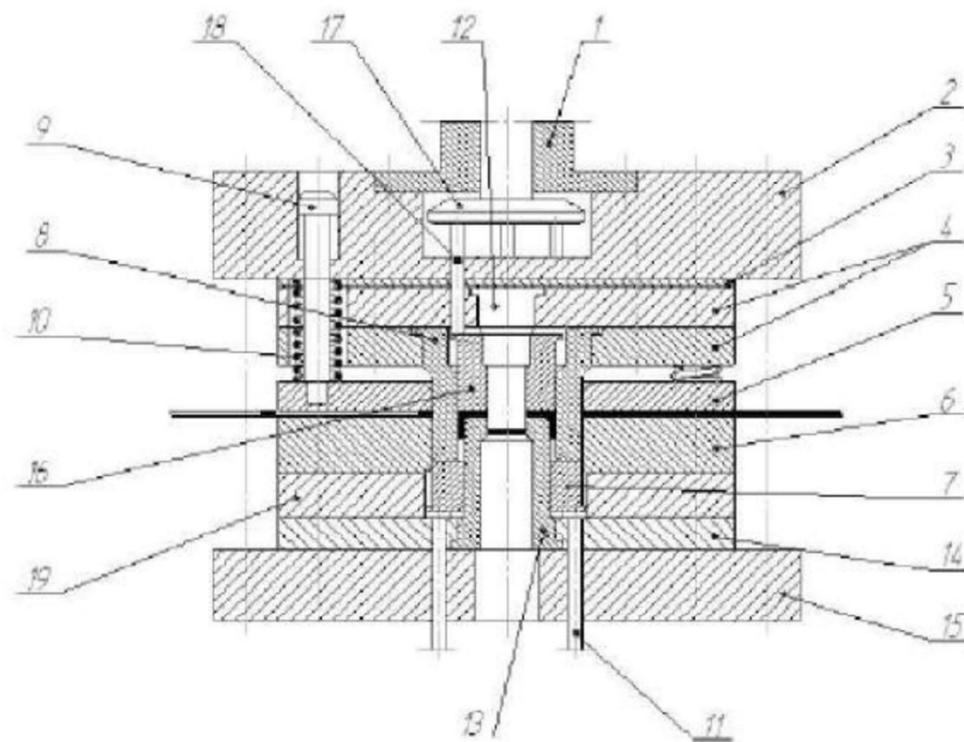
Схема штампа совмещённого действия для вырубki, вытяжки и пробивки
